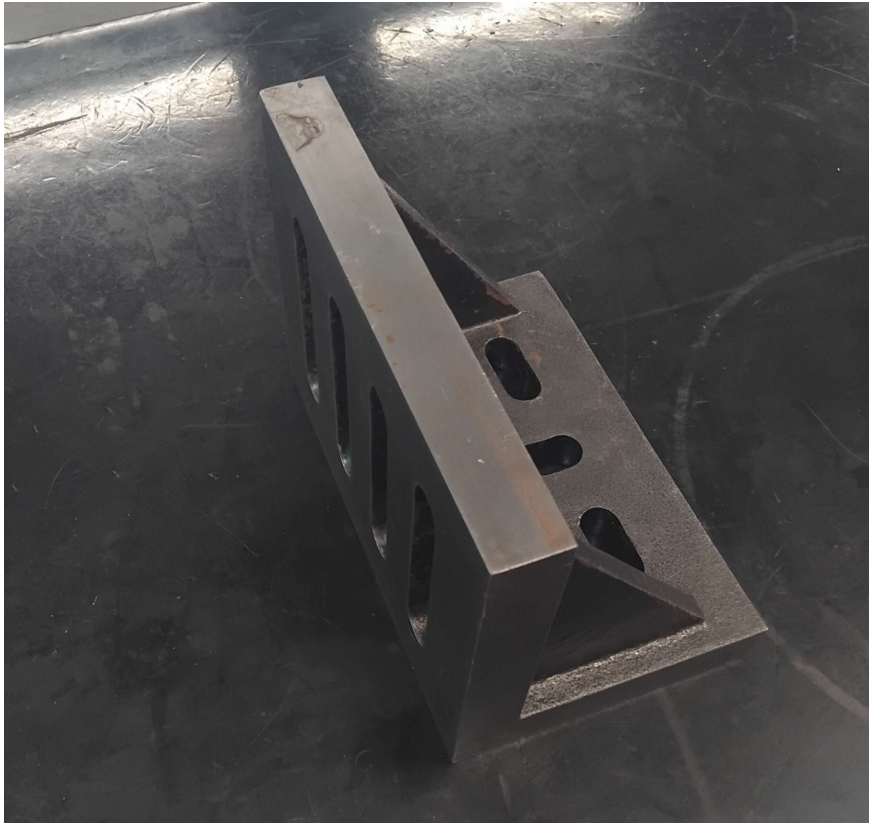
Image de l'équerre d'usinage sur lequel se monte le montage d'usinage (vue 1)
